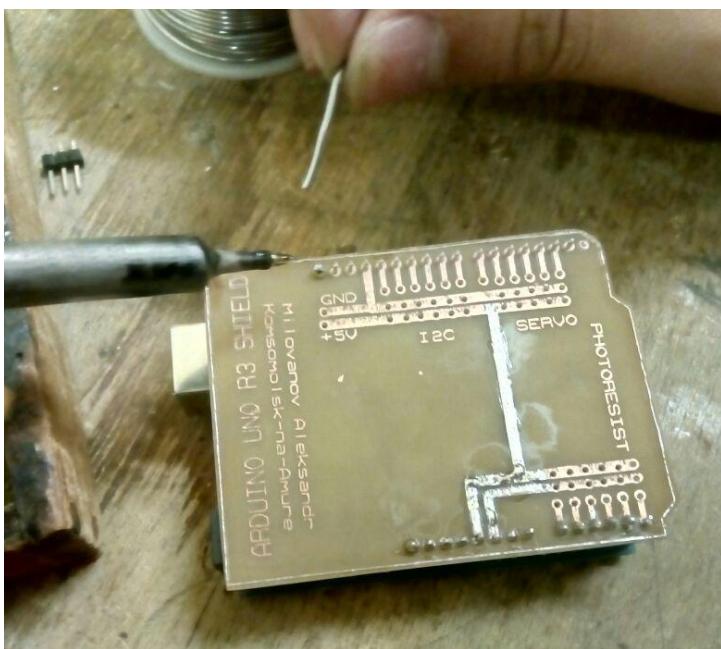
Этап №3. Изготовление печатной платы. Лужение платы. Пайка гребенки для присоединения к портам контроллера
